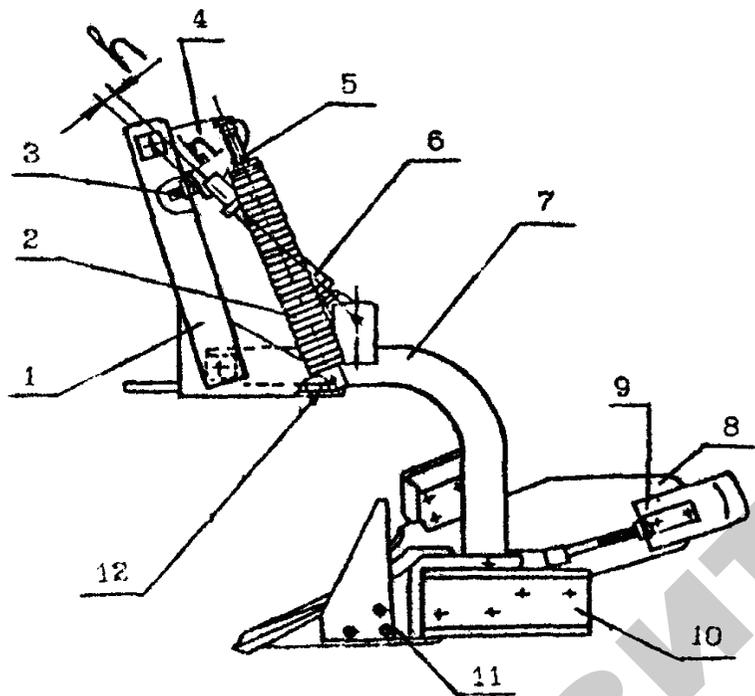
Механизм пружинный предохранительный корпуса плуга:
